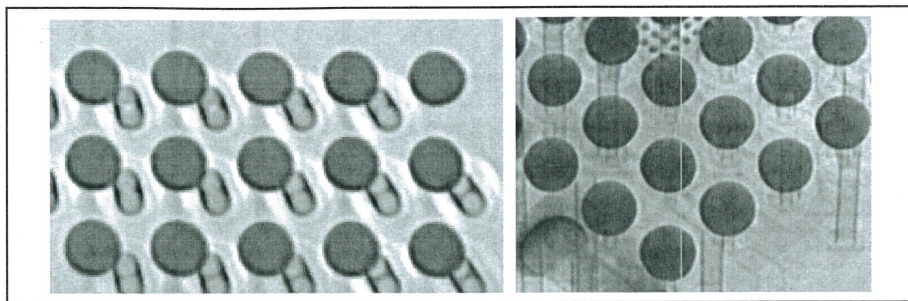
BGA(可塌落焊球)焊接理想状态图
